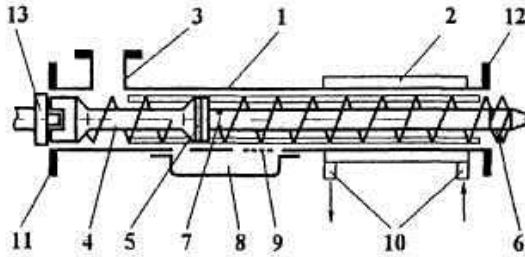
Схема пресувального шнека преса з вакуумуванням тіста у процесі пресування: 1 – циліндр; 2 – охолоджуюча сорочка; 3 – живильний патрубок; 4 – пресувальний шнек; 5 – роз'єднувальна шайба; 6 – тризахідна ланка шнека; 7 – отвір для приєднання вакуум-клапана; 8 – перепускний канал; 9 – розподільча решітка; 10 – штуцери для підведення і відведення охолоджуючої води; 11, 12 – приєднувальні фланці; 13 – вал редуктора преса
